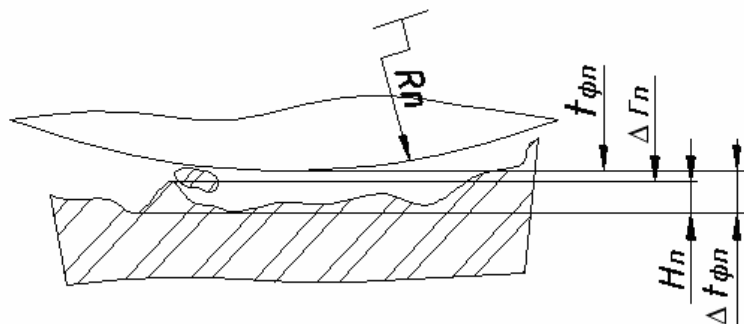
Схема взаємодії інструмента і заготовки при шліфуванні пористого заліза
